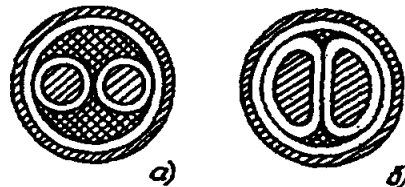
Двухжильные кабели с круглыми (а) и сегментными (б) жилами
